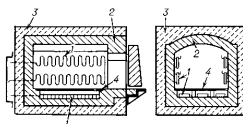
Печь сопротивления: 1 – электроды; 2 – тигель; 3 – теплоизоляция; 4 – жароупорная подовая плита
